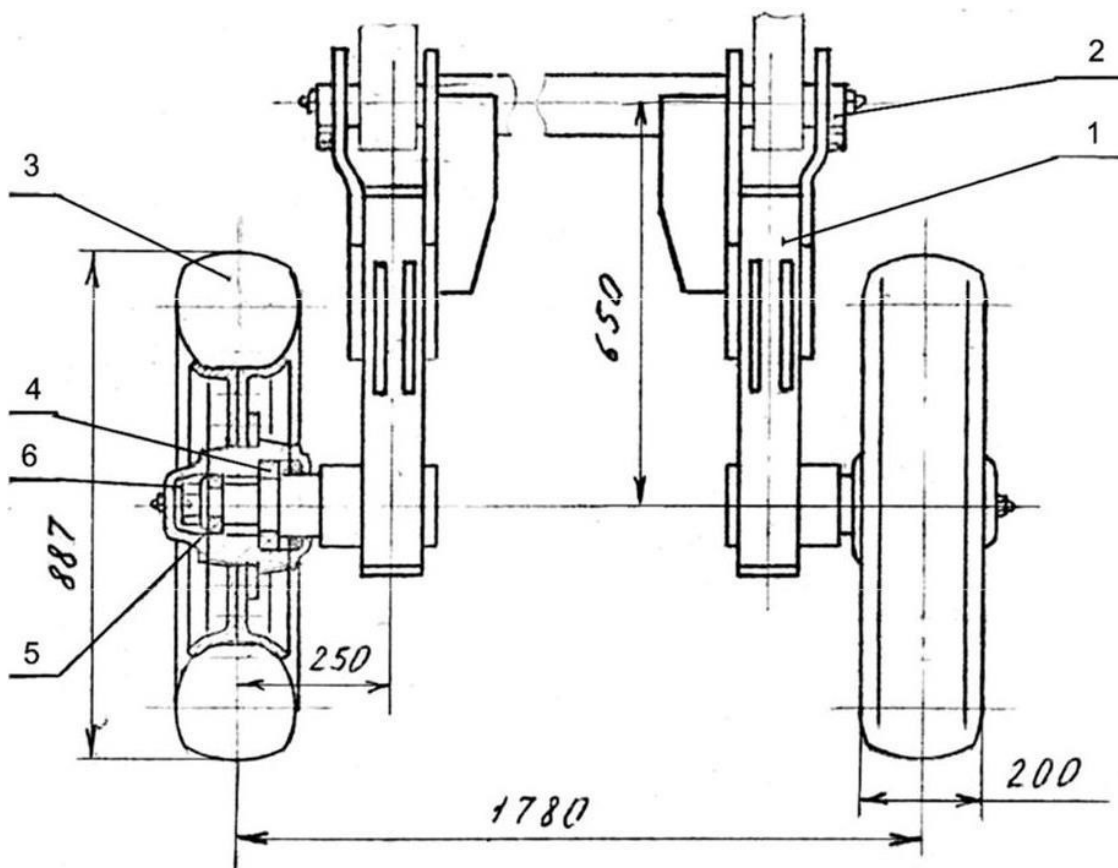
Шасси: 1 – траверса; 2 – ось; 3 – колесо ходовое; 4 – подшипник; 5 – подшипник; 6 – гайка
